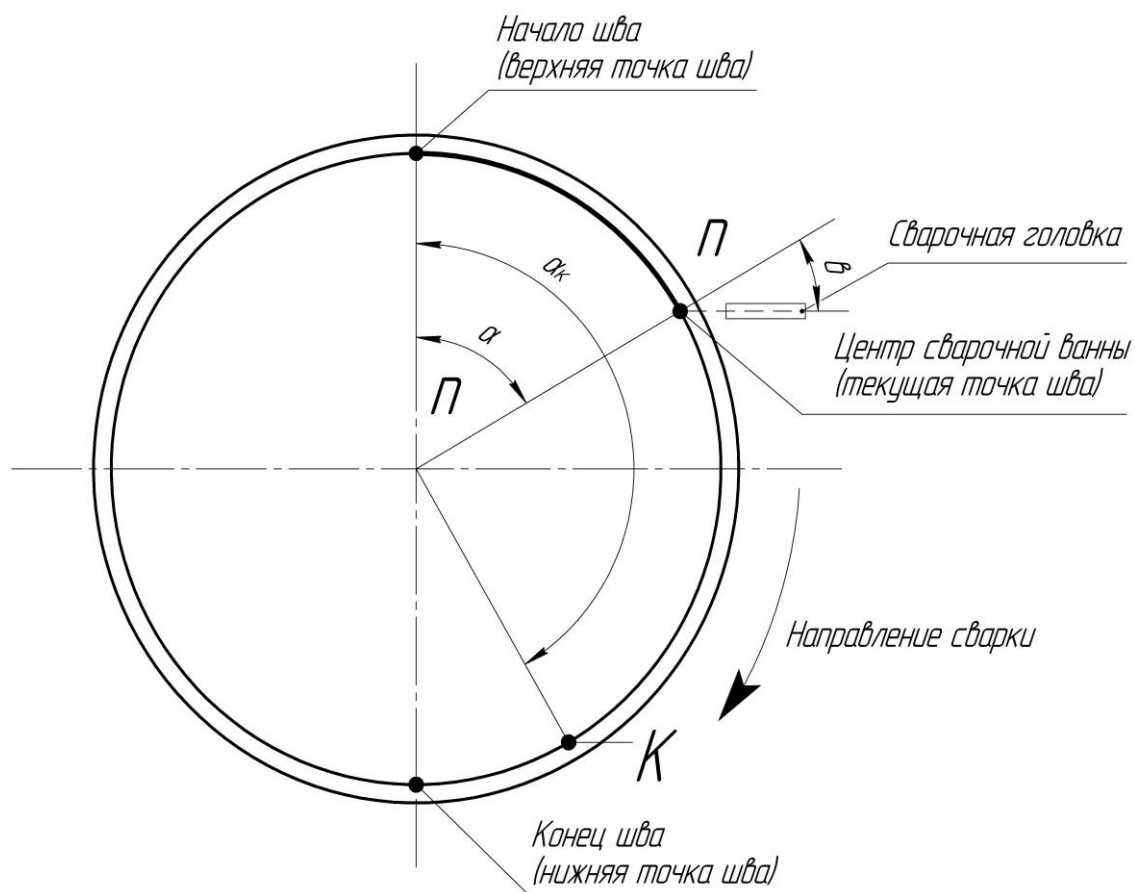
расположение сварочного шва на трубе.
